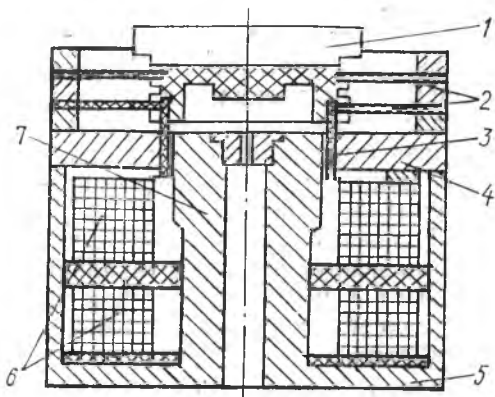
Электродинамический вибростенд: 1 — рабочий стол; 2 — мембрана; 3 — звуковая катушка; 4 — крышка; 5 — корпус; 6 — катушка электромагнита; 7 — керн
